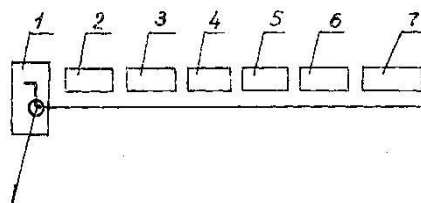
Структурная схема обозначения сварных швов на чертежах по ГОСТ 2.312–72
